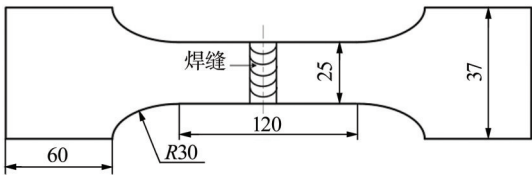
焊接接头拉伸试样尺寸(单位:mm)
